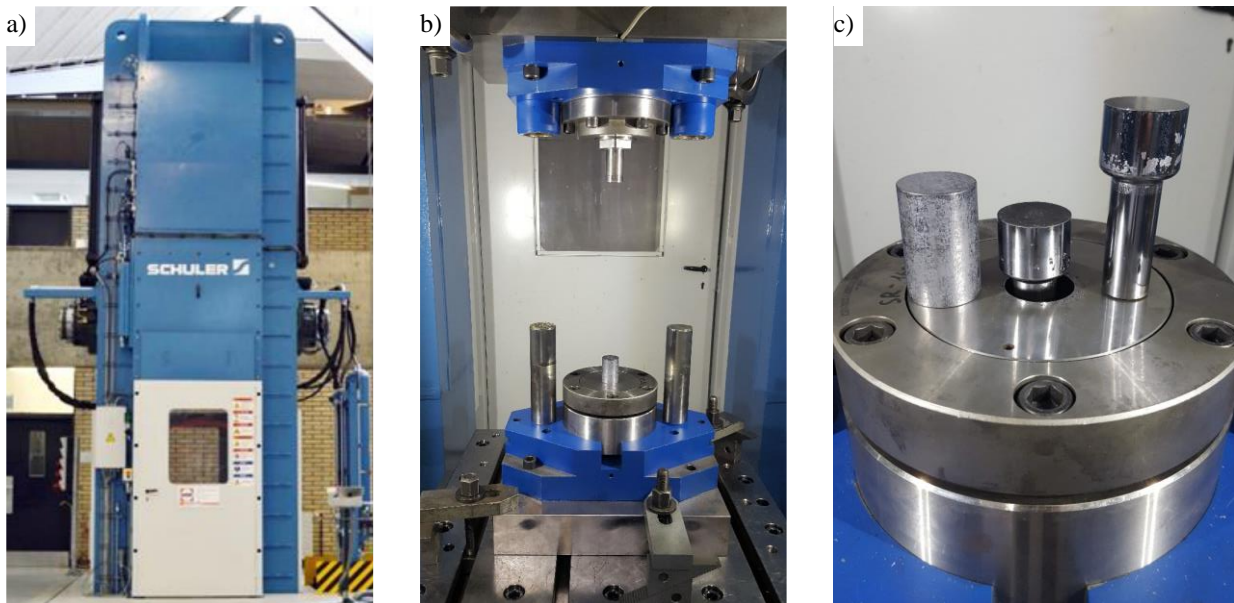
a) Servomechanische Presse am Institut für Umformtechnik b) Werkzeug vor Versuchsbeginn c) Rohteil und Pressteile
